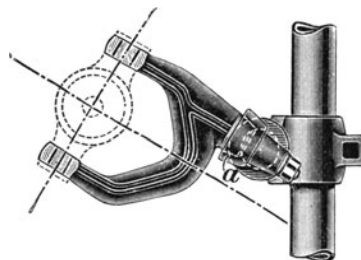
Gabel-Aufhängung für Schrämmaschinen.
